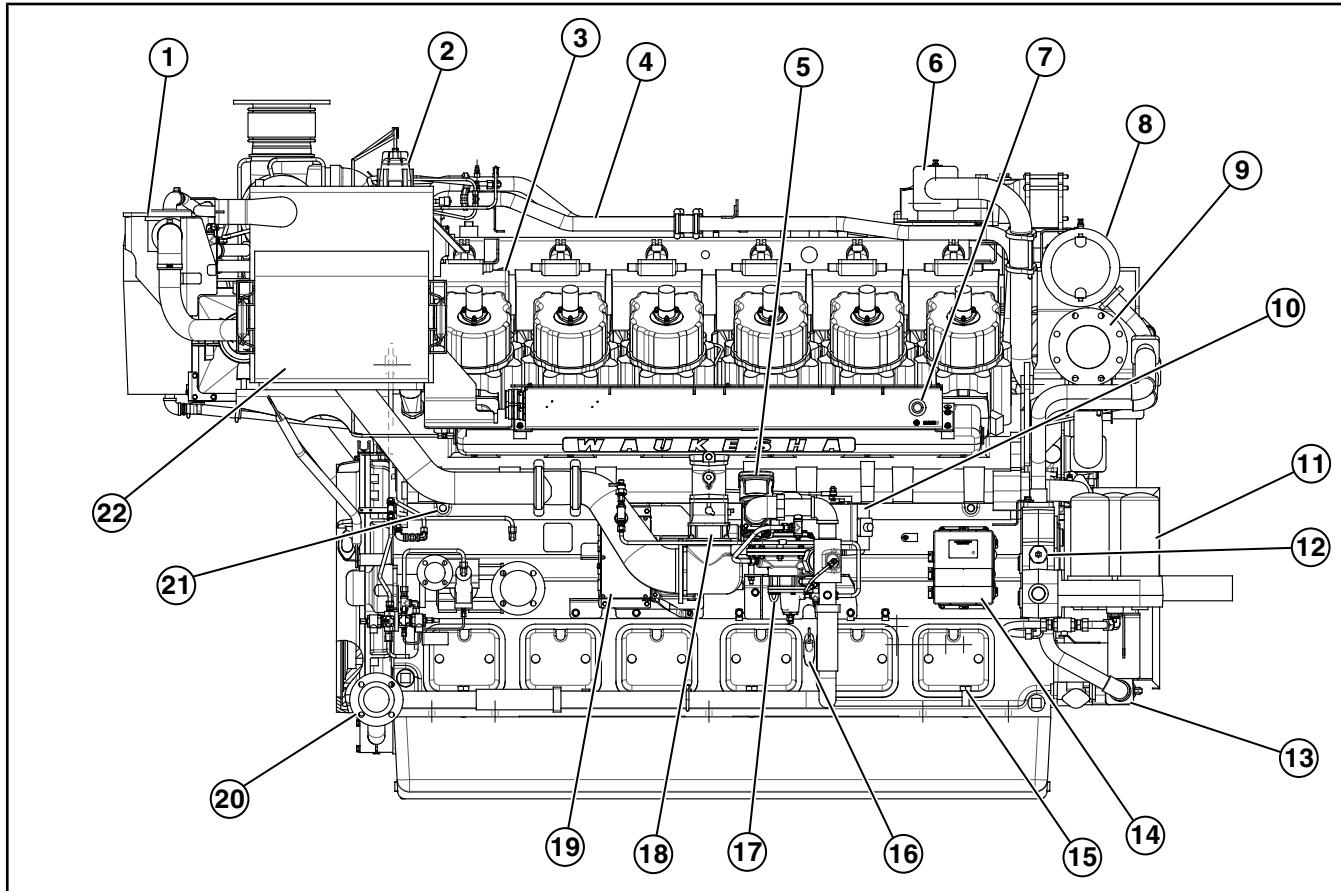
Вид справа (двигатель L7044GSI)
